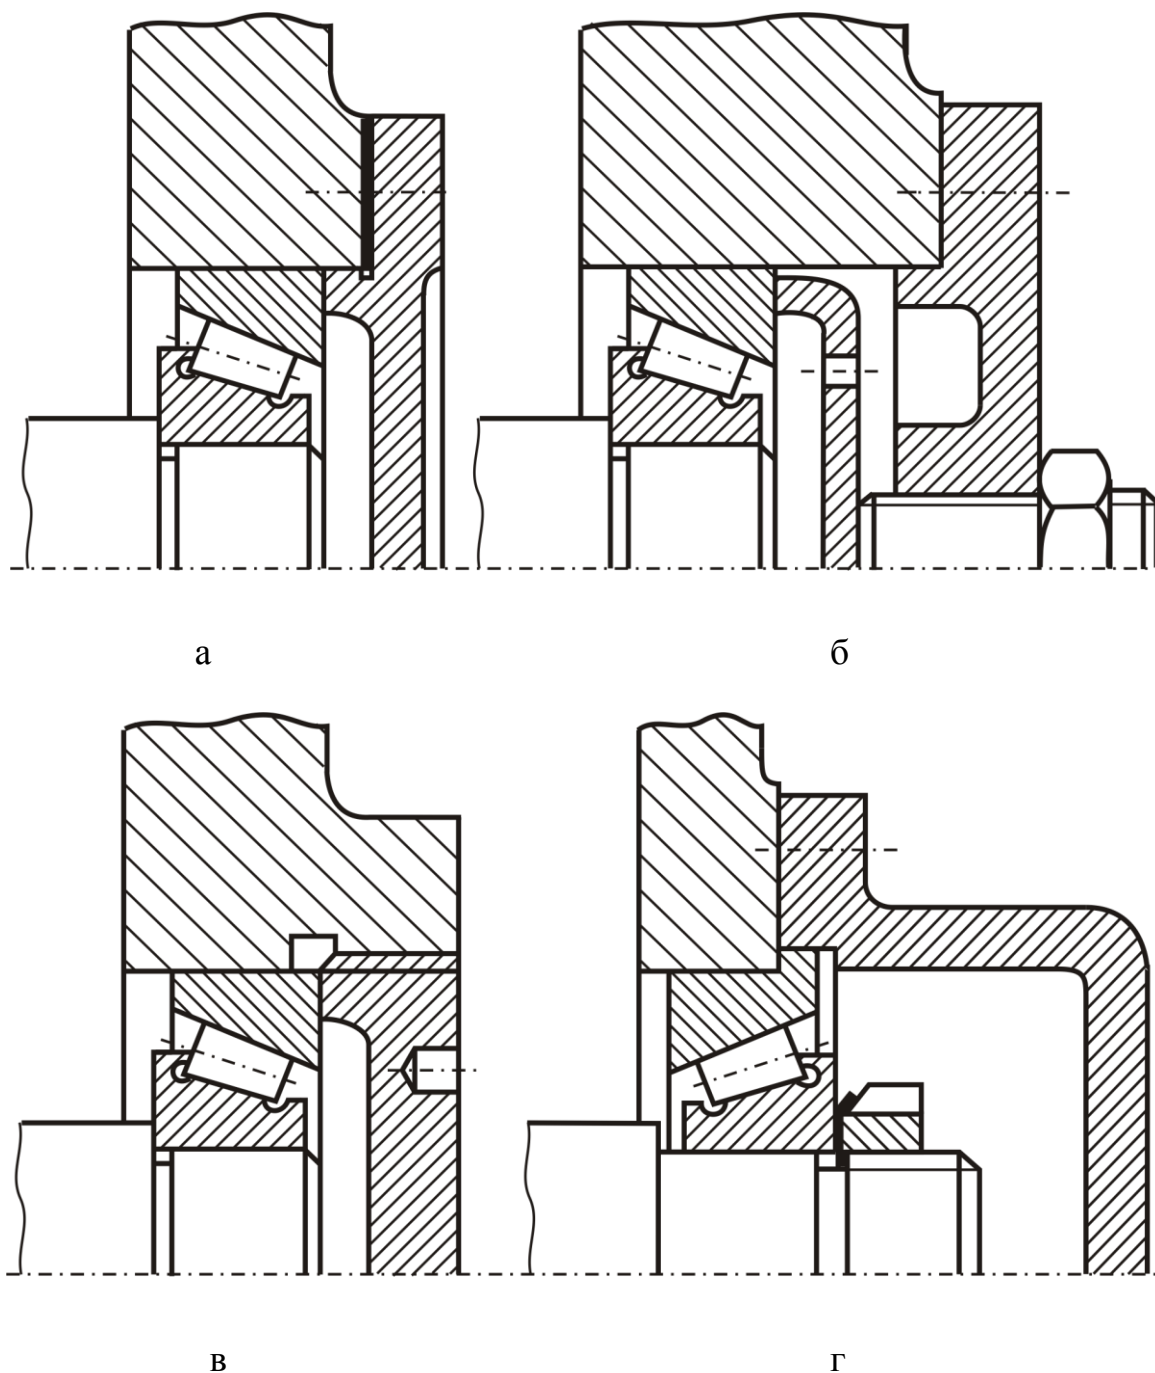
Способы регулирования зазора в конических роликоподшипниках:
